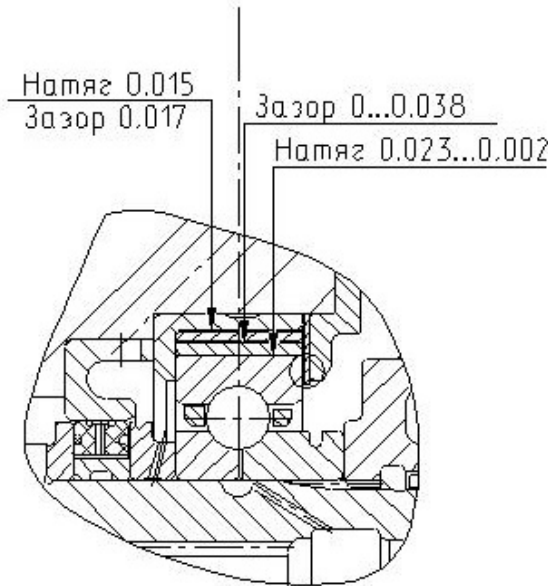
Конструкция опоры роторов 1 и 2 с подшипником 74-126708P
